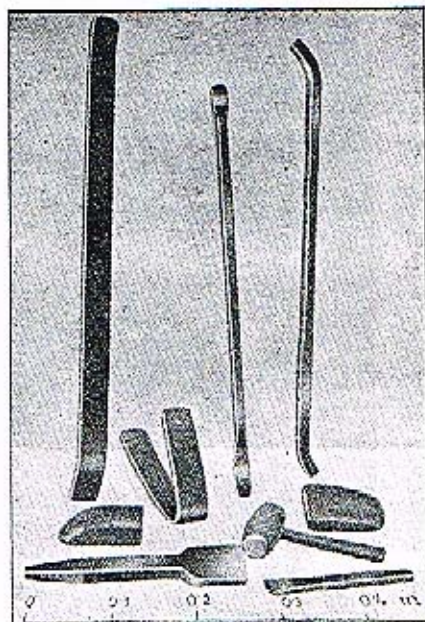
Páka k hrubému vyrovnávání předních částí blatníku
